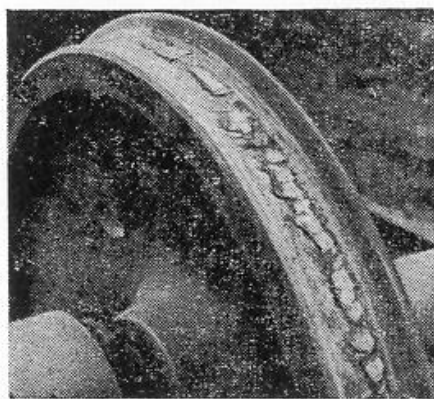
Дефект на поверхности катания колеса, вызванный смещением металла - «навар»
